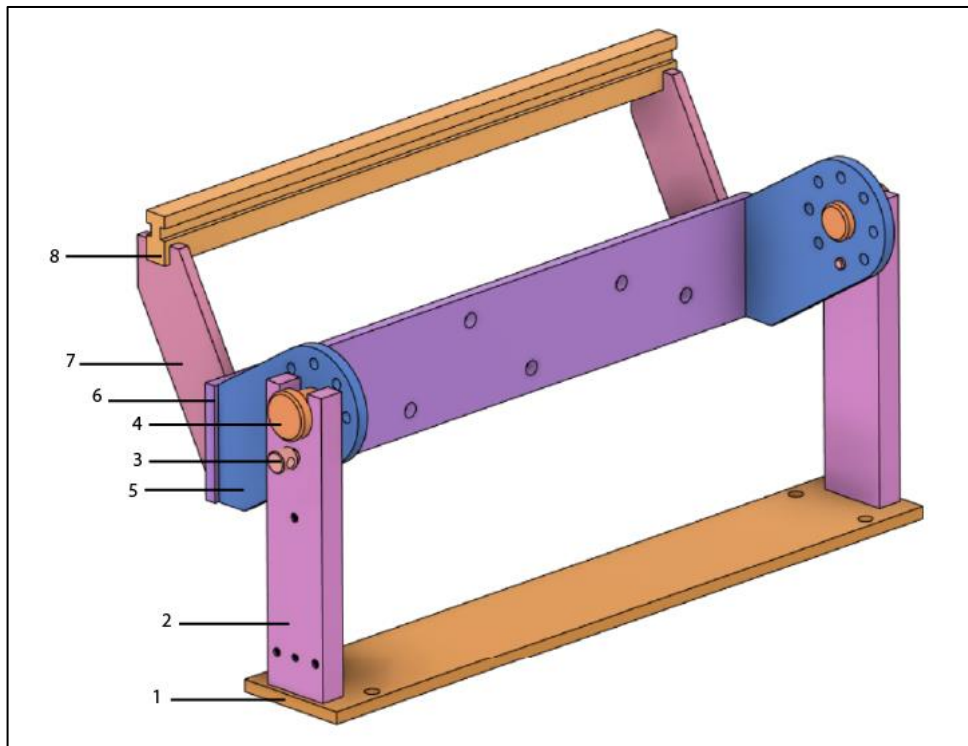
Сборка модели стенда для обслуживания и ремонта головок блоков цилиндров: 1 – основание, 2 – стойка (2 шт.), 3 – стопорный винт (2 шт.), 4 – цапфа (2 шт.), 5 – пластина (2 шт.), 6 – несущая пластина, 7 – опора направляющей (2 шт.), 8 – направляющая.
